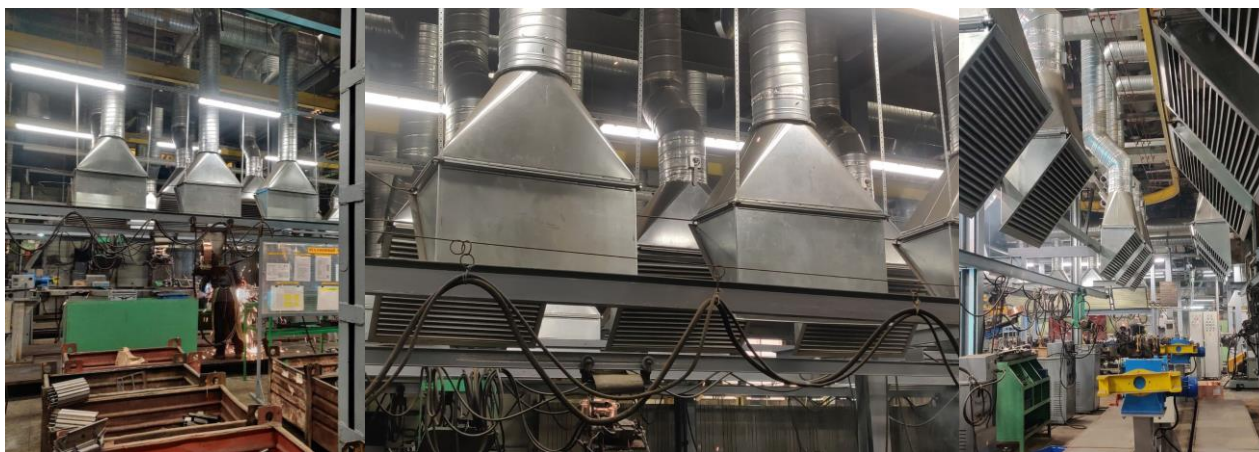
Сварочный цех ООО «УАЗ-Штамповочное производство» [7]
